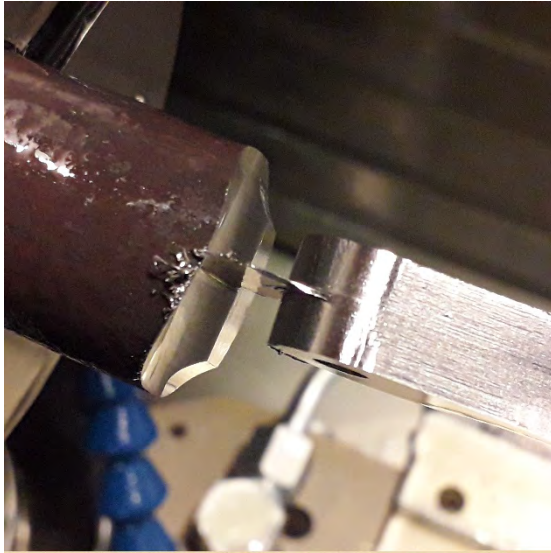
Отрезка готовой детали «кошачий коготь»
